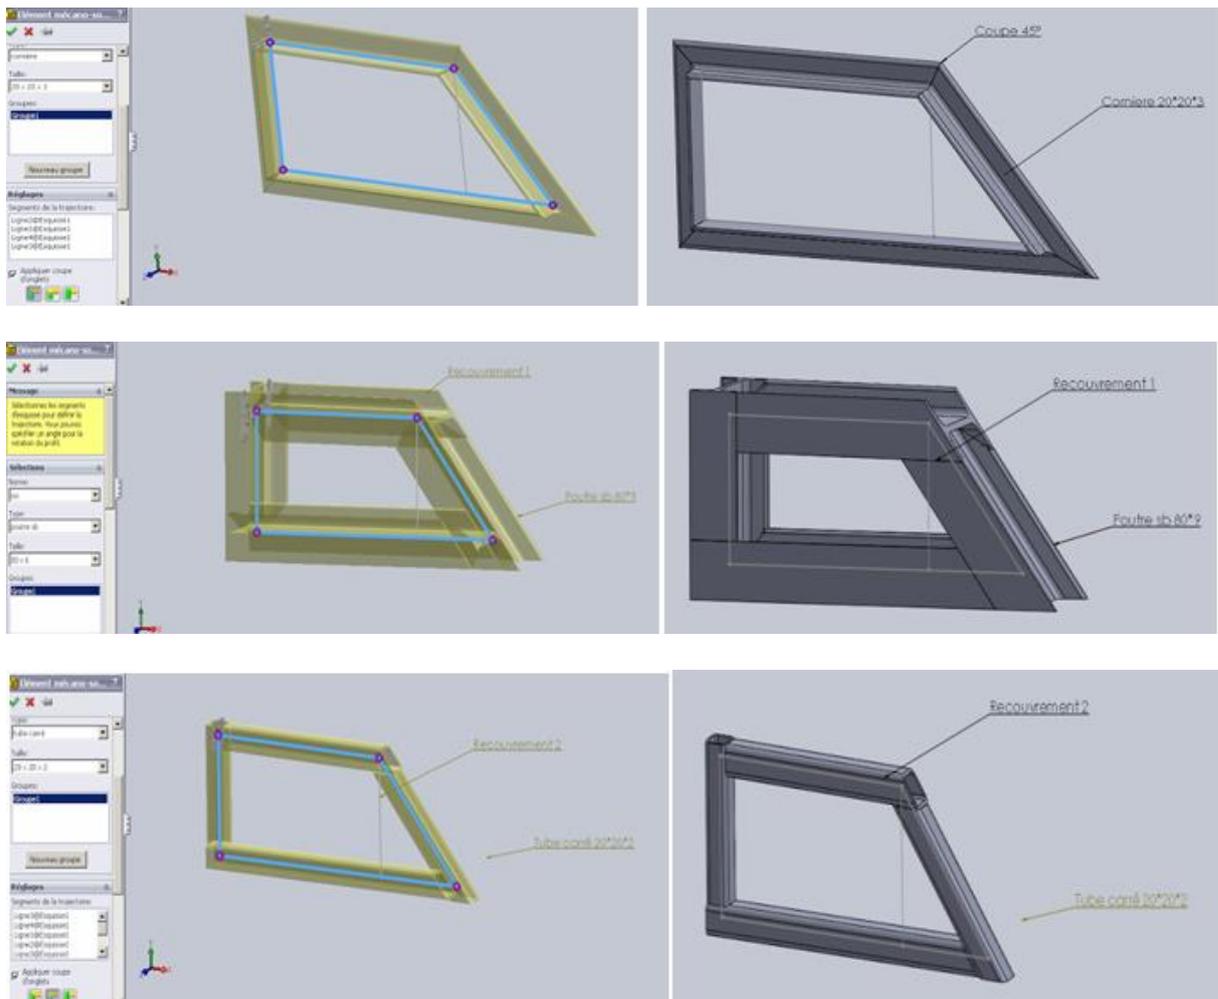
b- Construction soudée avec différents Recouvrements.
